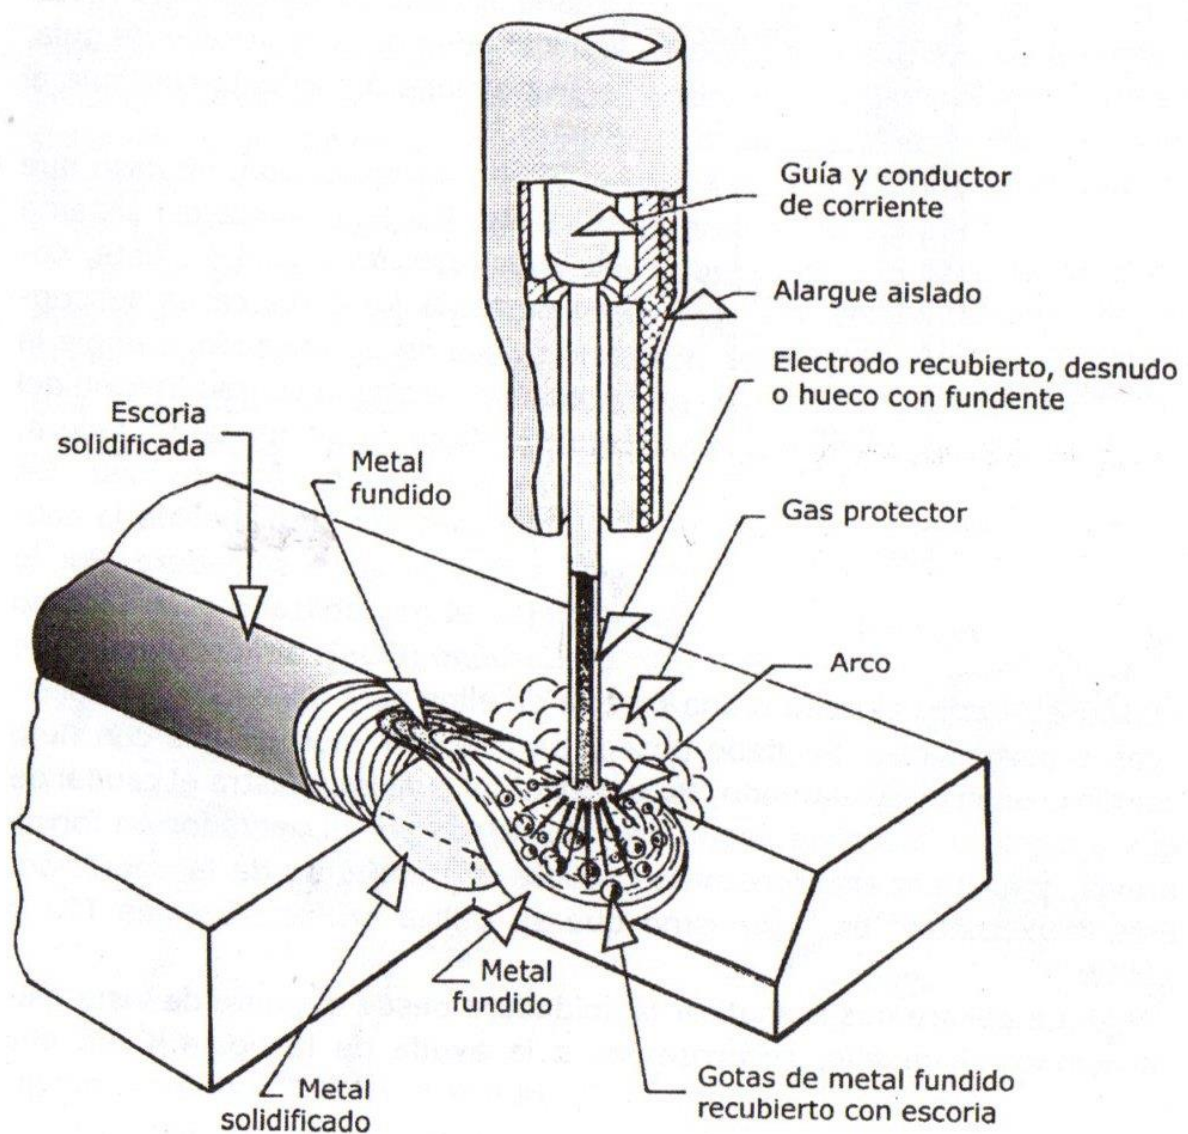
Ilustración del proceso de fusión en la soldadura MIG
